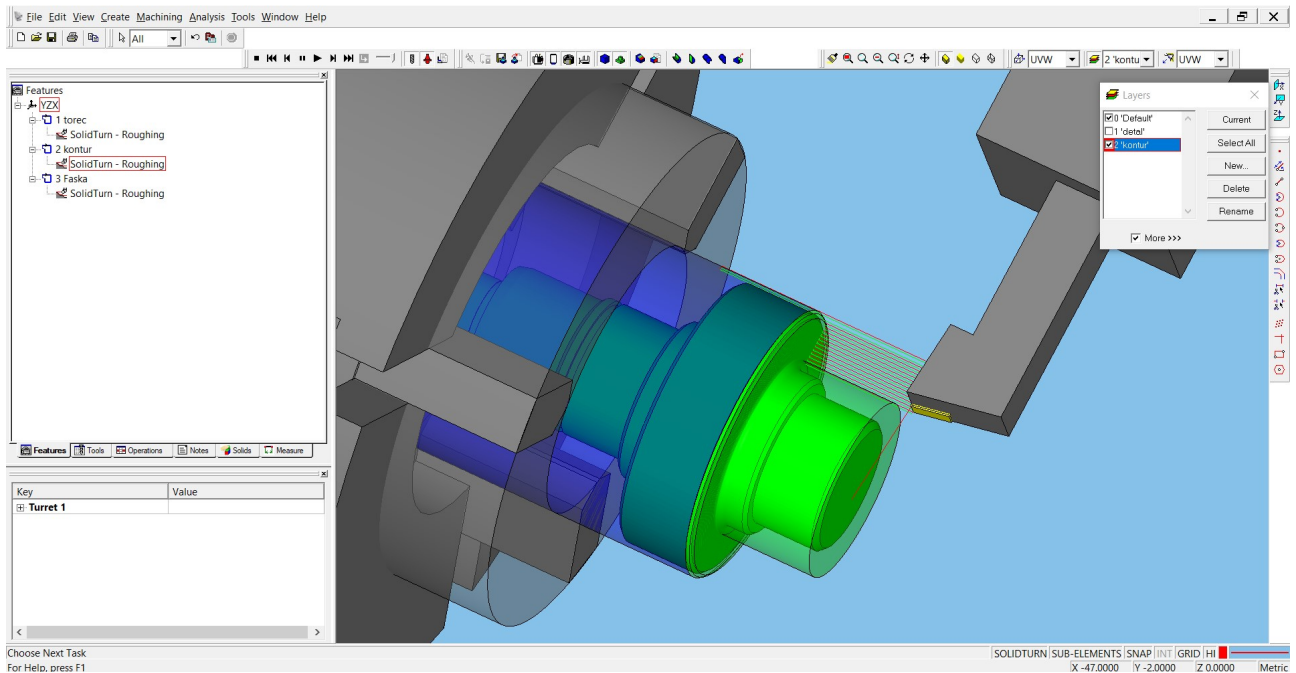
Траєкторія руху металорізального інструменту при обробленні контуру вала-шестерні
